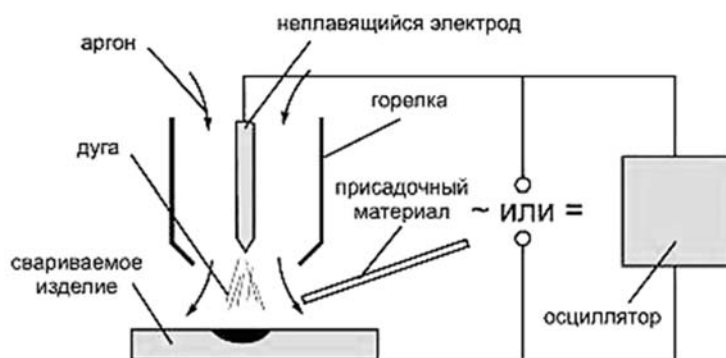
Схема процесса сварки в защитных газах неплавящимся электродом
